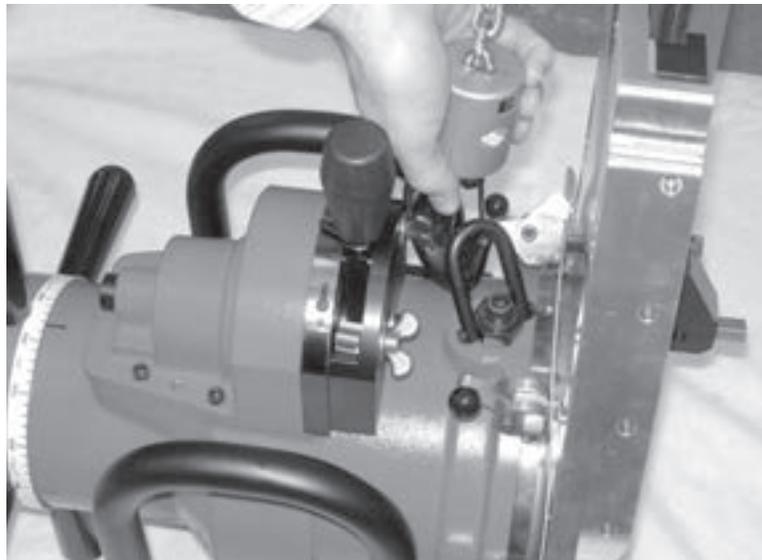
Sujete el dispositivo de elevación al cáncamo de elevación.
